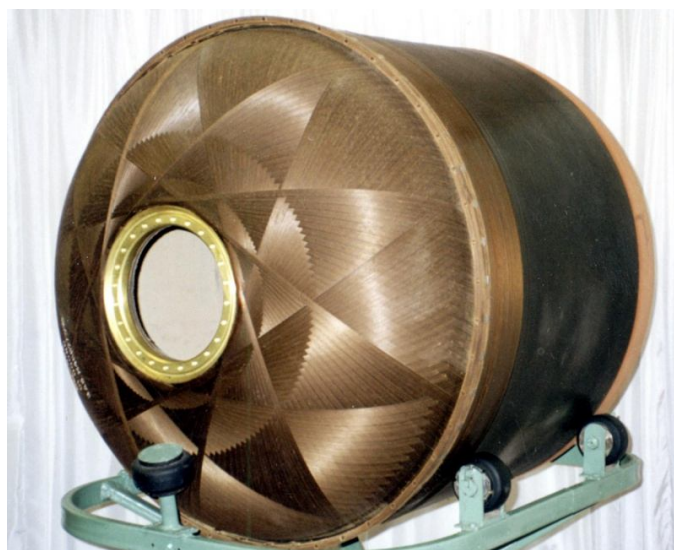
Корпус ракетного двигателя твердого топлива, изготовленный методом СПН
